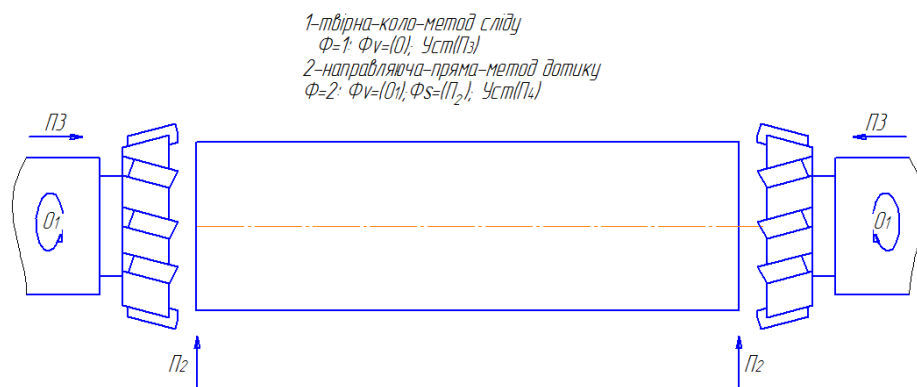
Комплекс формоутворюючих рухів при обробці нерухомої заготовки торцевими фрезами
